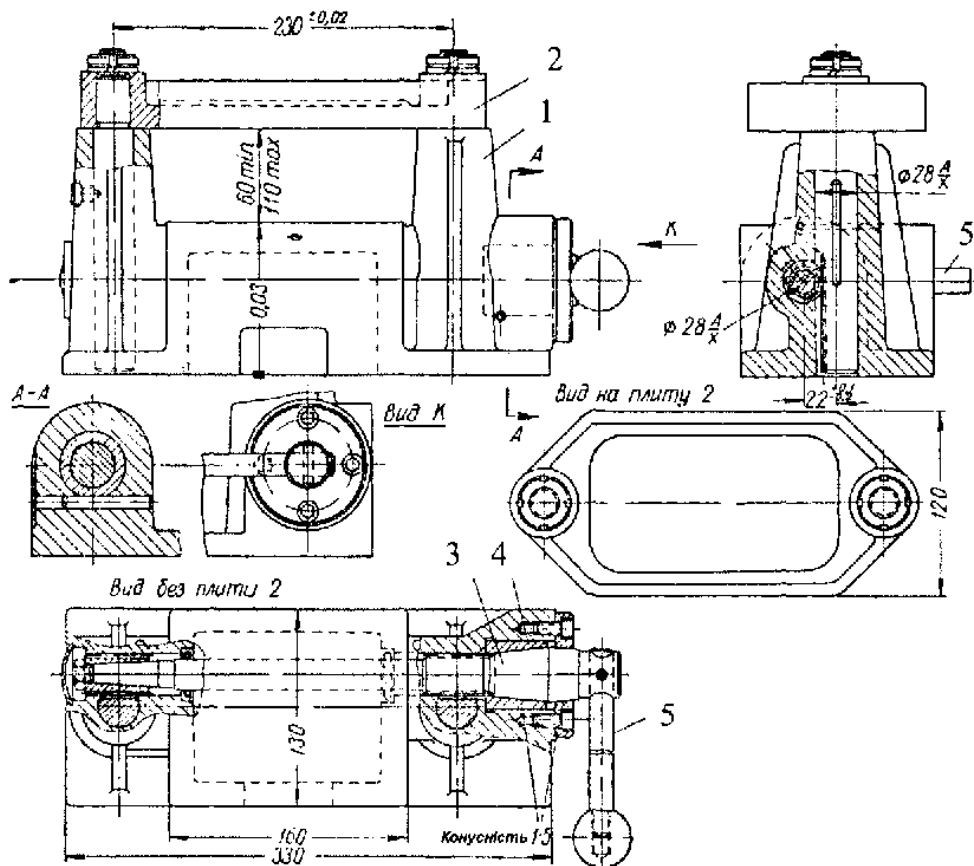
Портальний скальчастий кондуктор з рейково-конусним механізмом
